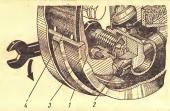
Регулировка вазора между колодквин и тормозным барабаном автомобили ГАЗ-09: 1- регулировчимй винт; 2- разжимной палец; 3- барабан; 4- накладка колодки.
